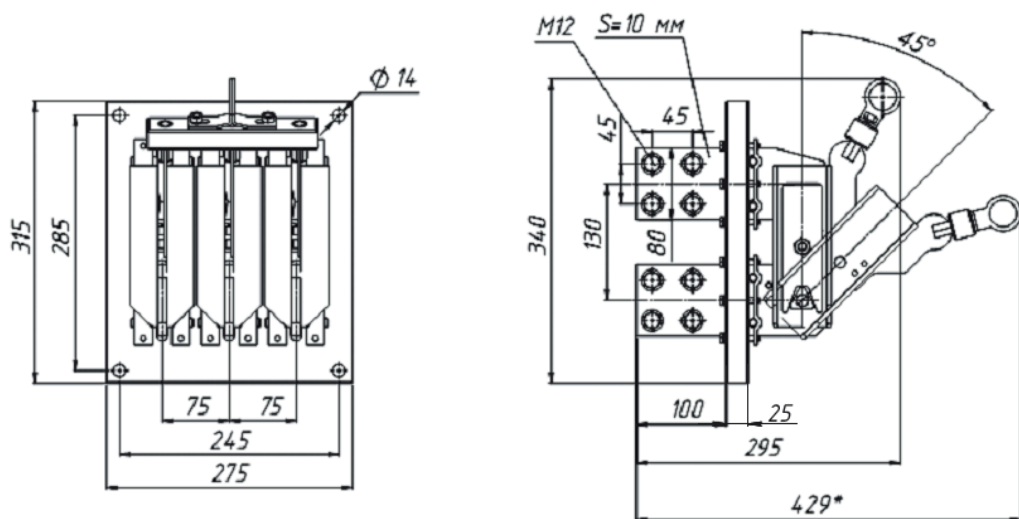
Разъединитель РЕ19 с рукояткой для пополюсного оперирования
